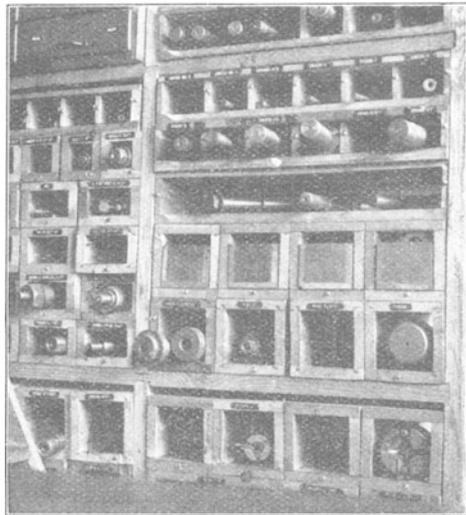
Aufbewahrung von Werkzeugen in der Werkzeugstube.
